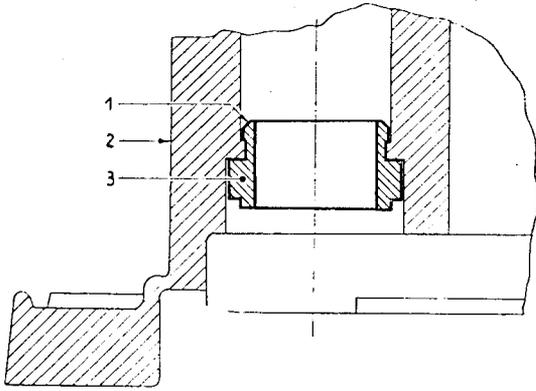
Richtig eingeschlagener Einlaßventilsitz
